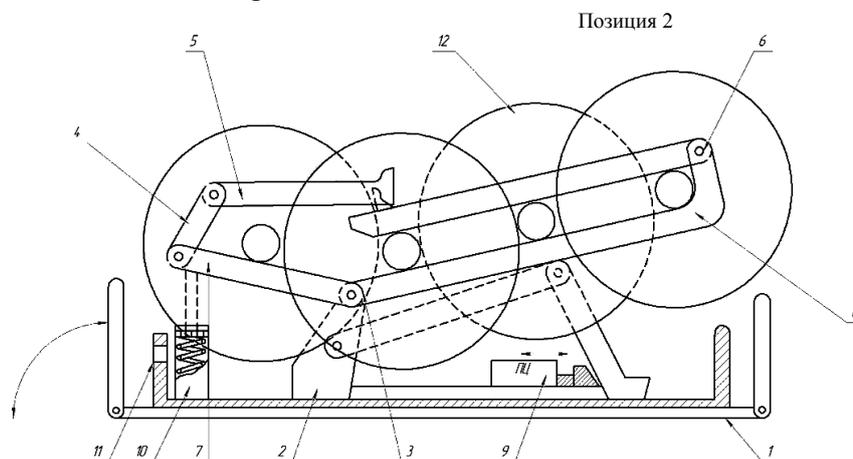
Устройство для погрузки - выгрузки колёсных пар на транспортном средстве - вид с торца
